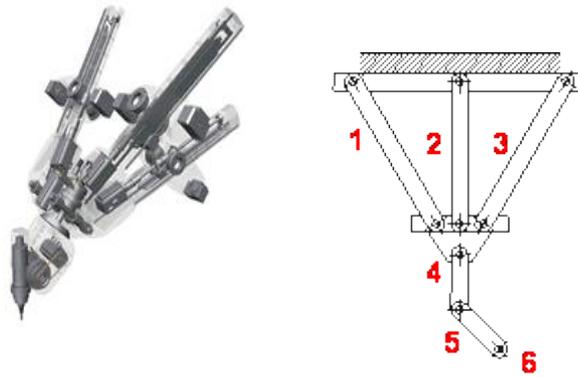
а) Механизм для обработки зубчатого колеса, б) схема механизма обработки.
